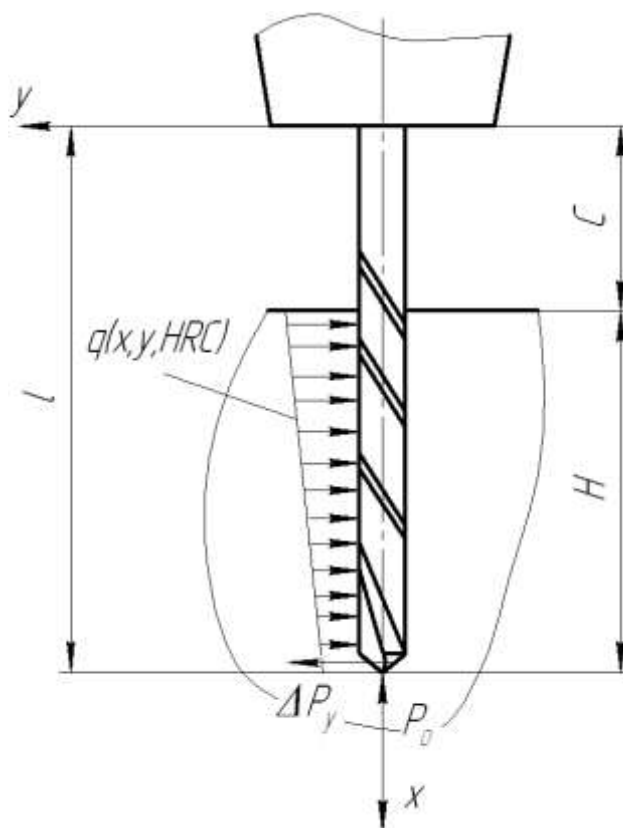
Розрахункова схема для визначення деформації свердла
